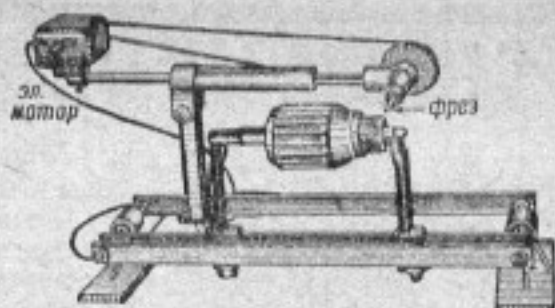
Станок для фрезеровки изоляции между коллекторными пластинами
